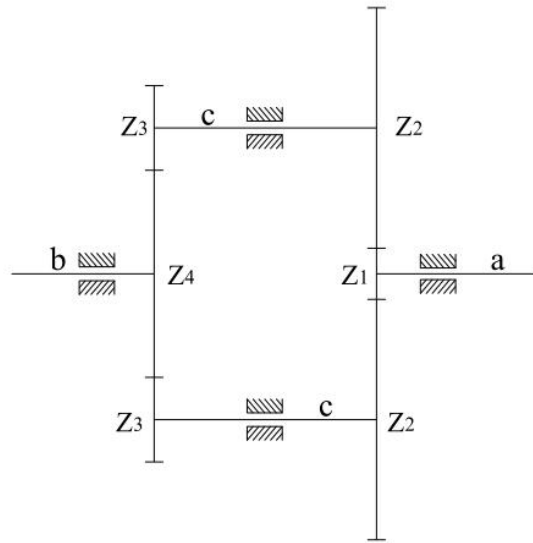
两级分流式圆柱齿轮减速装置传动简图
